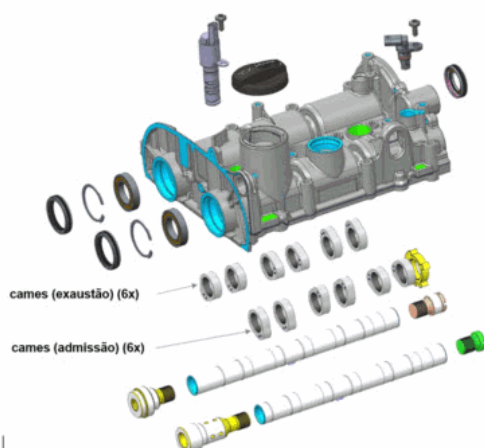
aplicação do came no módulo de comando de válvulas (vista explodida).
